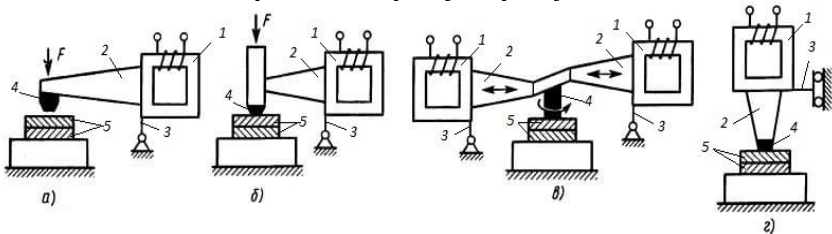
Основные схемы типовых установок для УЗС металлов: а) продольная; б) продольно-поперечная; в) продольно-вертикальная г) крутильная [3].
